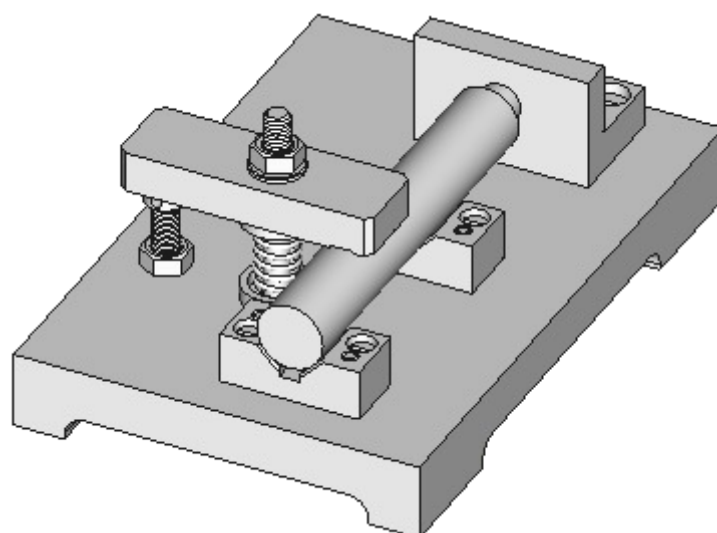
Установка цилиндрической заготовки на 2 призмы; торец цилиндра соприкасается с опорой, установленной в кронштейне
